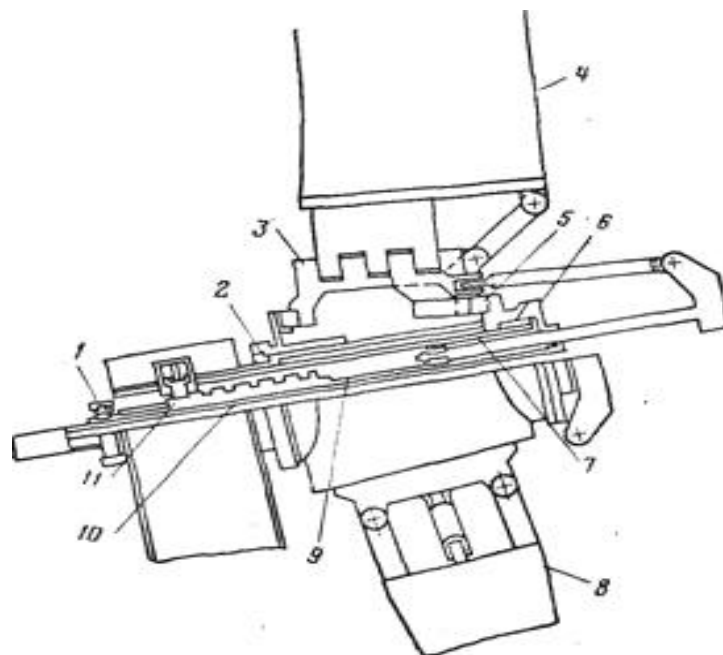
Центральна частина вітроколеса (вид в розрізі): 1 - коромисло механізму регулювання; 2 - задній підшипник втулки; 3 - затискачі; 4 - лопать (у флюгерному положенні); 5 - підшипник лопасті; 6 - передній підшипник втулки; 7 - шпindel; 8 - лопать в робочому положенні; 9 - тяга механізму регулювання; 10 - головний порожнистий вал; 11 - гвинтовий паз механізму автоматичної зупинки вітроколеса.
